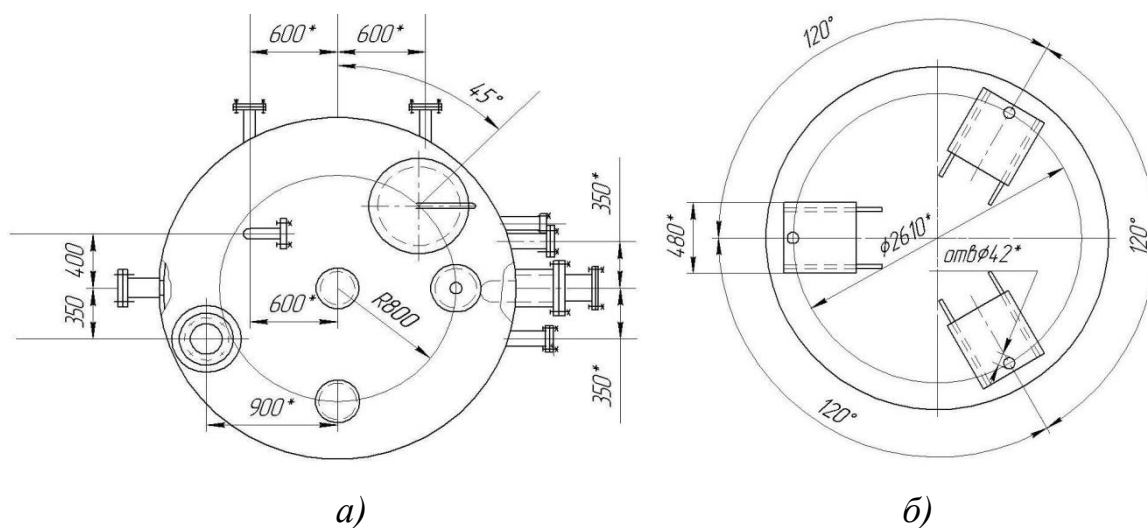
Вид корпуса сверху, вид А (а) и вид Б (б)
